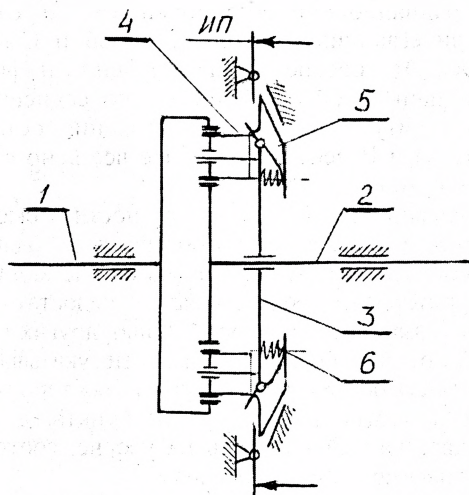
1, 2 — ведущее и ведомое колеса; 3 — водило; 4 — сателлиты; 5 — стопор; 6 — пружина; ИП — исполнительный механизм
